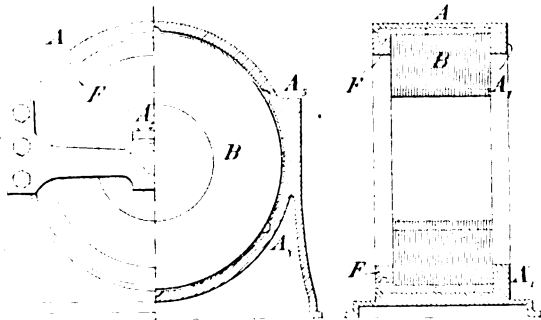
et 5. — Coupes et vue d'un inducteur Soames à tôles fixées par métal fusible.
